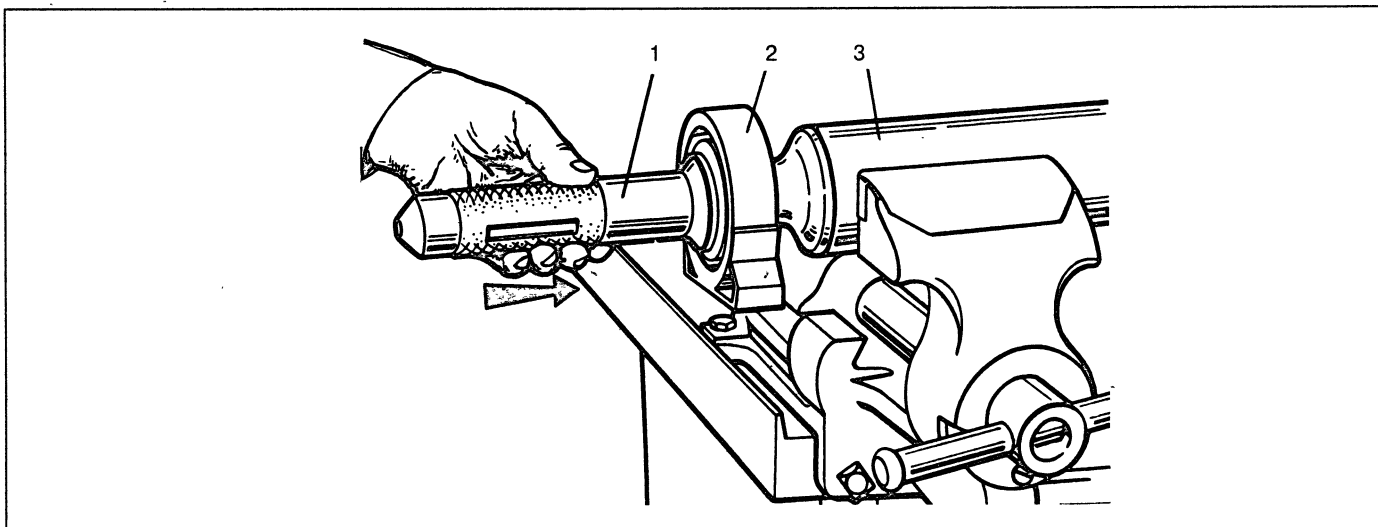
Извлечение стопорного кольца подшипника упругой опоры: 1 – стопорное кольцо; 2 – подшипник; 3 – упругая опора
